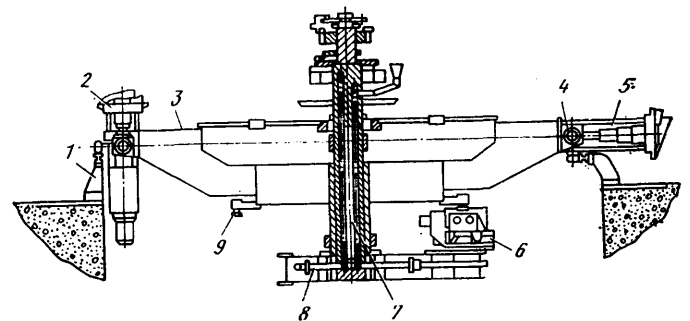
Карусельно-кокильная машина для литья ступиц: 1 — копи; 2 — неподвижная плита; 3 — сектор; 4 — подшипник; 5 — кокильная секция; 6 — привод поворота; 7 — колонна; 8 — рама; 9 —
